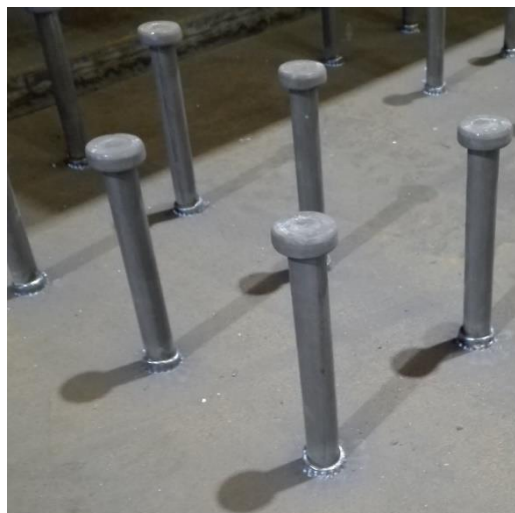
Soldadura de conetores (Processo 783)
